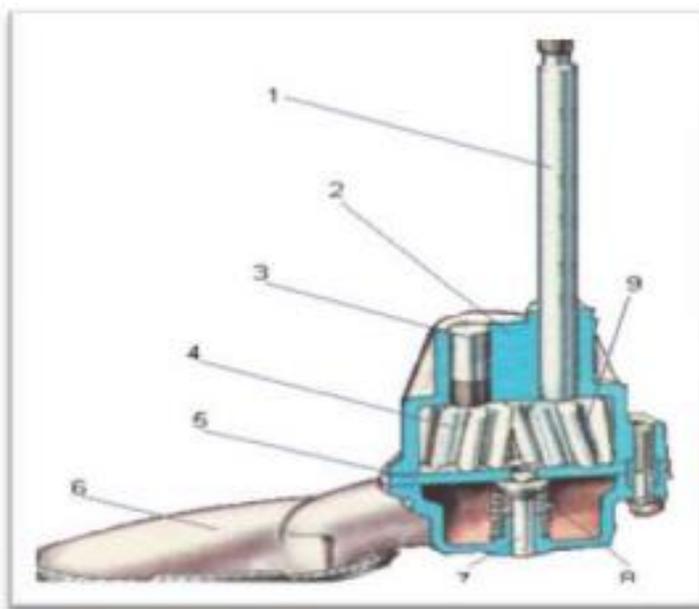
Устройство односекционного масляного насоса: 1- ведущий вал масляного насоса; 2 - корпус масляного насоса; 3 - ось ведомой шестерни; 4 - ведомая шестерня; 5 – проставка; 6 – маслоприёмник; 7 - редукционный клапан; 8 - пружина редукционного клапана; 9 - ведущая шестерня
